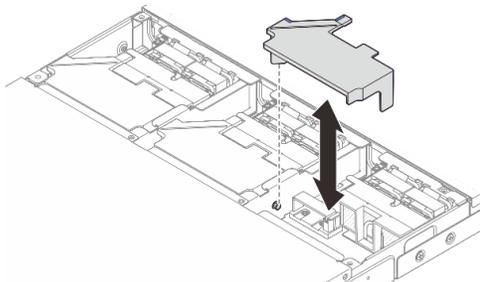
Installieren der Luftführung für das 1U2N-Gehäuse
